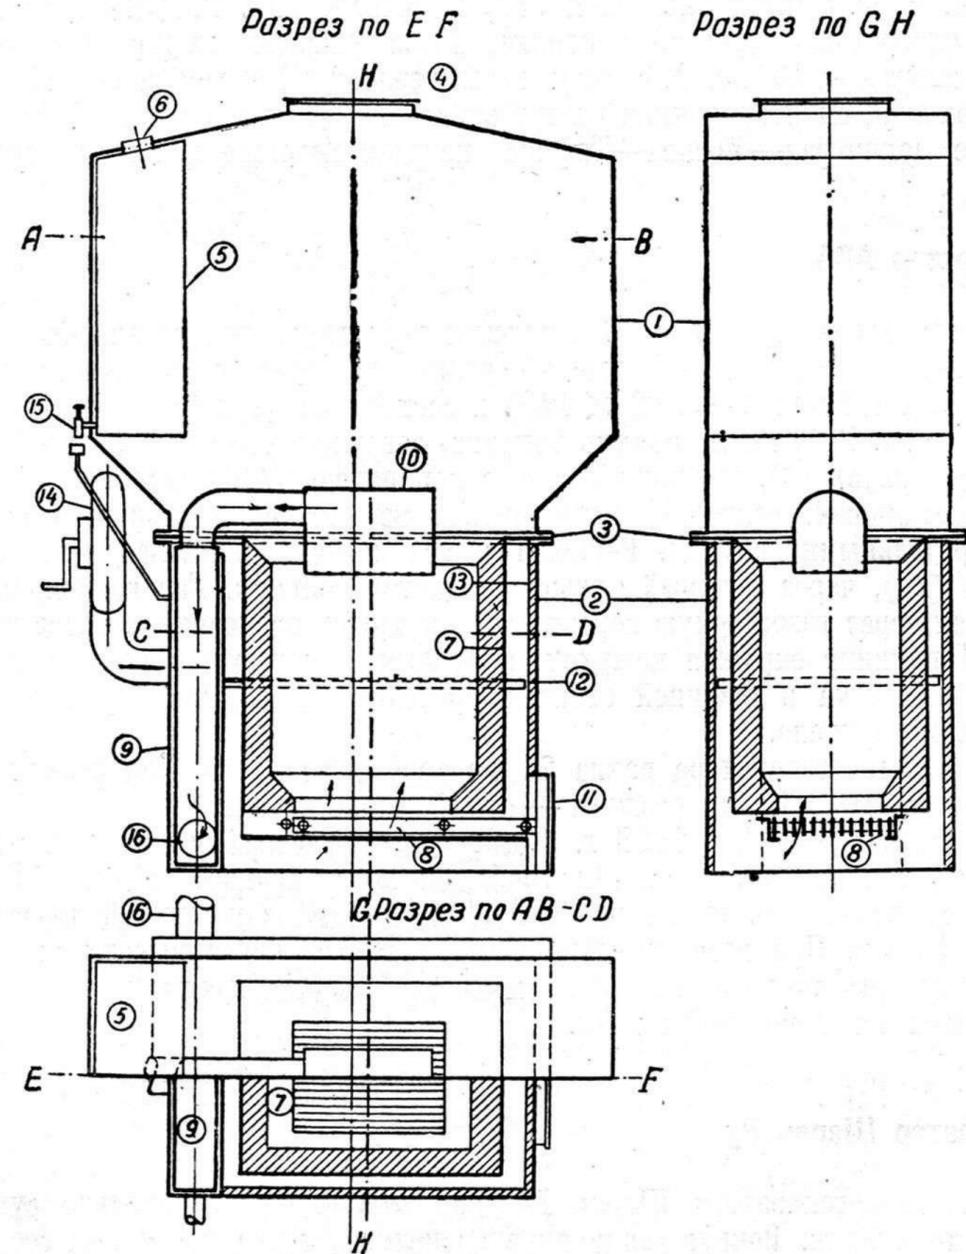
Газогенератор АРА. 1—верхний кожух газогенератора; 2—нижний кожух газогенератора; 3—скрепление верхней и нижней части; 4—загрузочный люк; 5—водяной резервуар; 6—заливная пробка; 7—топливник; 8—колосниковая решетка; 9—испаритель; 10—газосборная коробка; 11—зольниковый люк; 12—асбестовая изоляция; 13—железный лист изоляции; 14—вентилятор; 15—водопровод; 16—газопровод к двигателю
